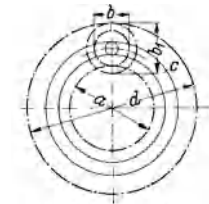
Einfaches Umlaufgetriebe mit Innenverzahnung und mit gestuften Umlaufrädern.
